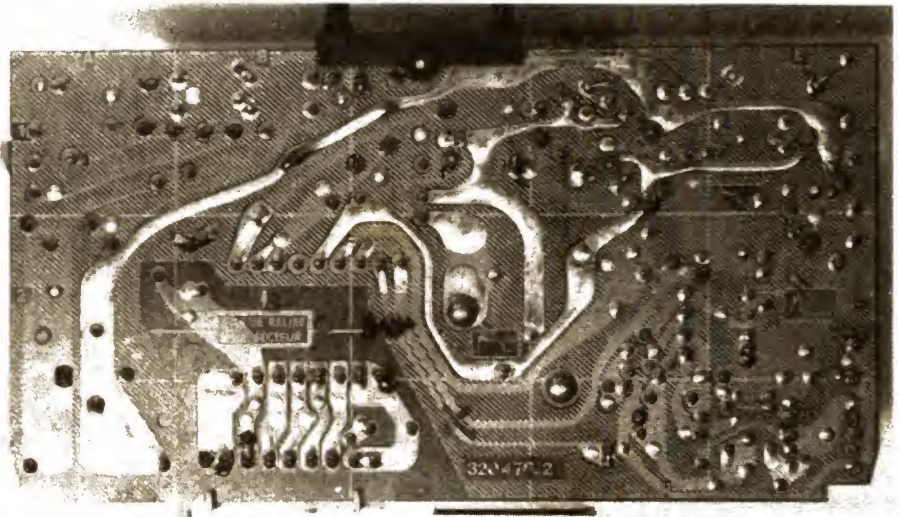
Photo C. — Le module « alimentation » vu côté circuit imprimé et soudures.
